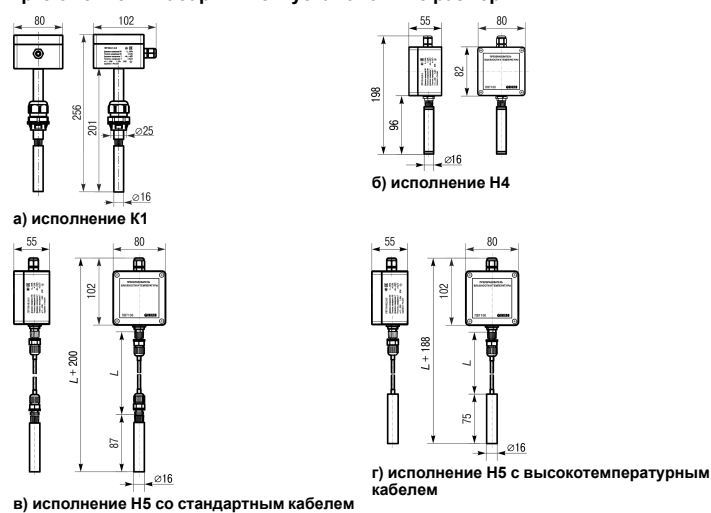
Габаритные и установочные размеры прибора (где L – длина кабеля выносного зонда)
